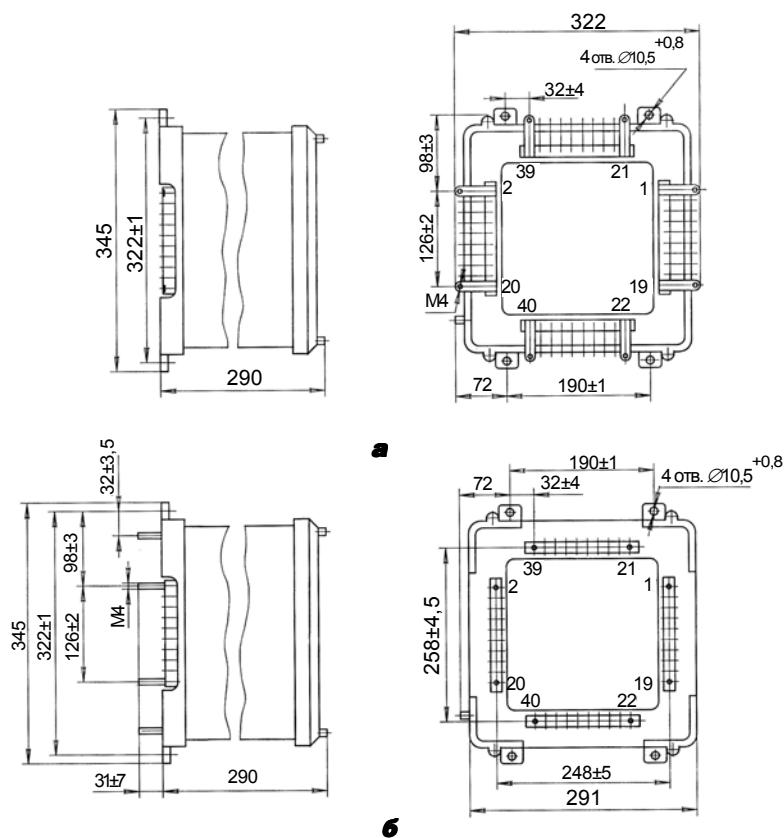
Габаритные, установочные и присоединительные размеры комплектов защиты типа КЗ-17.
